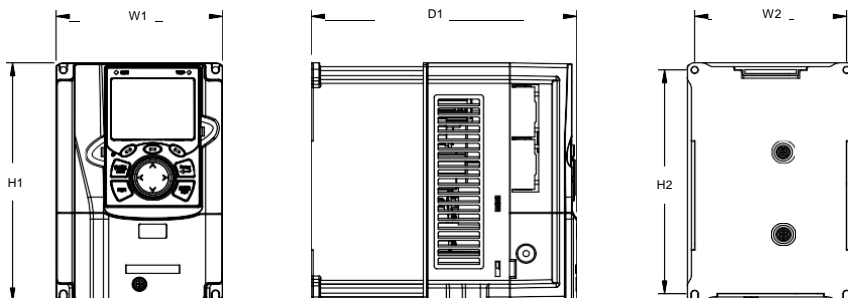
Схема настенного монтажа ПЧ напряжением 380 В, от 1,5 до 37 кВт
